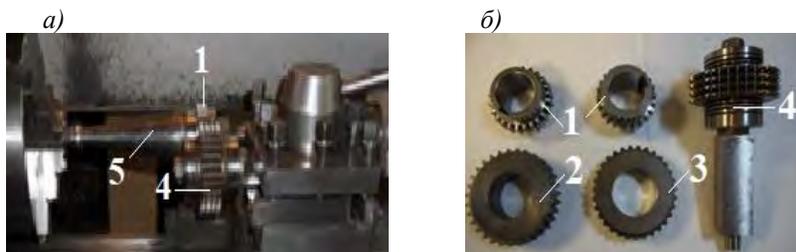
Процесс обработки, конструкция обкатного инструмента и обработанные заготовки: а – процесс обработки; б – конструкция обкатного инструмента и обработанные заготовки; 1 – обработанные зубчатые колеса Ст40Х, $m = 2 \div 5$, $z = 24$; 2 – шевер-прикатник Р6М5; 3 – шевер-прикатник ШХ15; 4 – инструмент в сборе; 5 – оправка для установки заготовки
